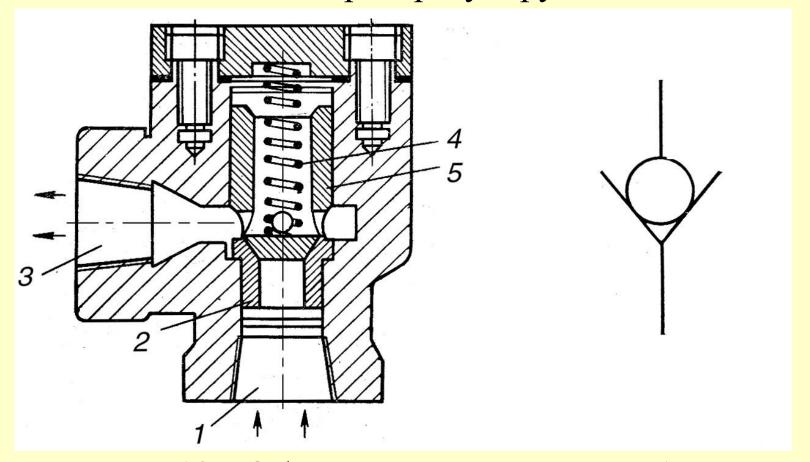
Обратный клапан типа Г51: а - конструкция; б - условное обозначение
